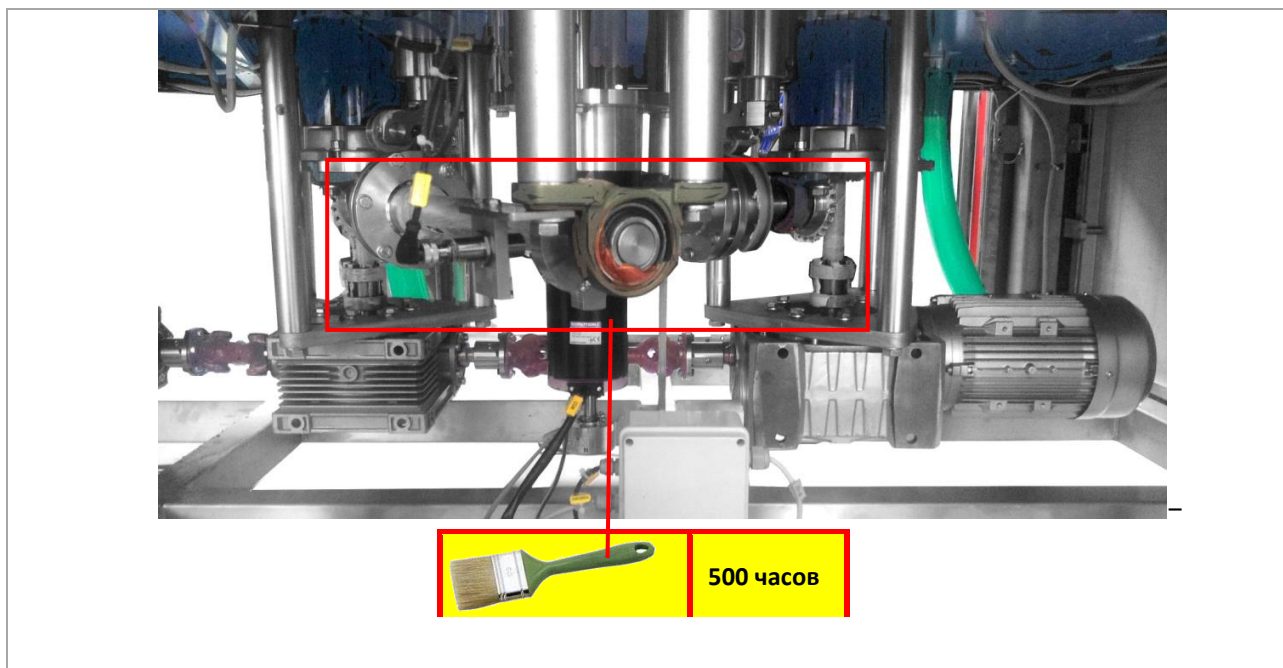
Смазка трансмиссии колонн группы закатки
